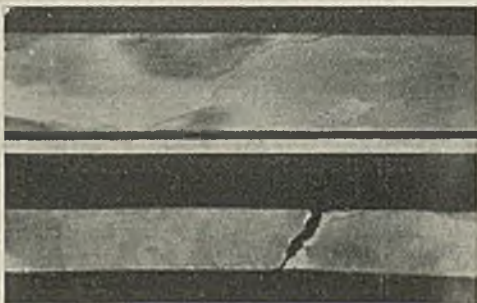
Gut ausgeführte Wassergasschweißung.
